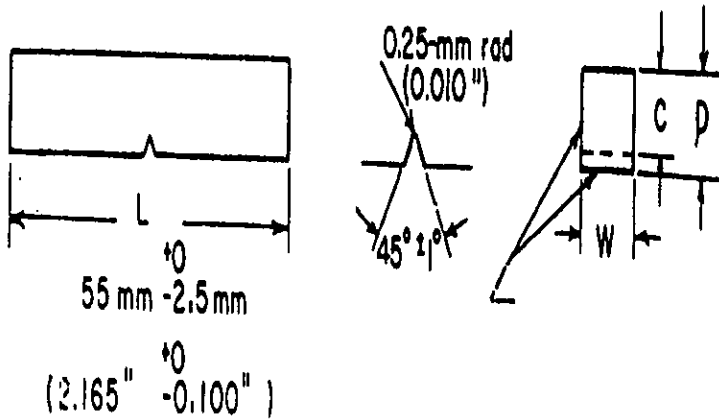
Probetas para el ensayo de impacto Charpy.
